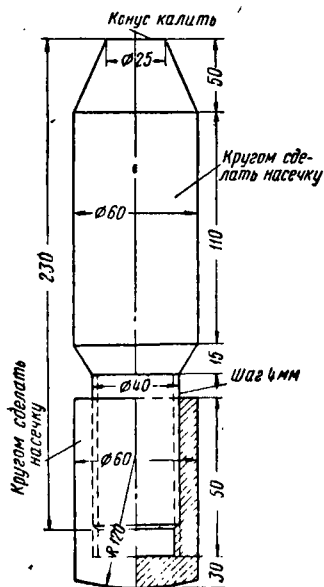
Приспособление для клепки планок носиков тягового двигателя
